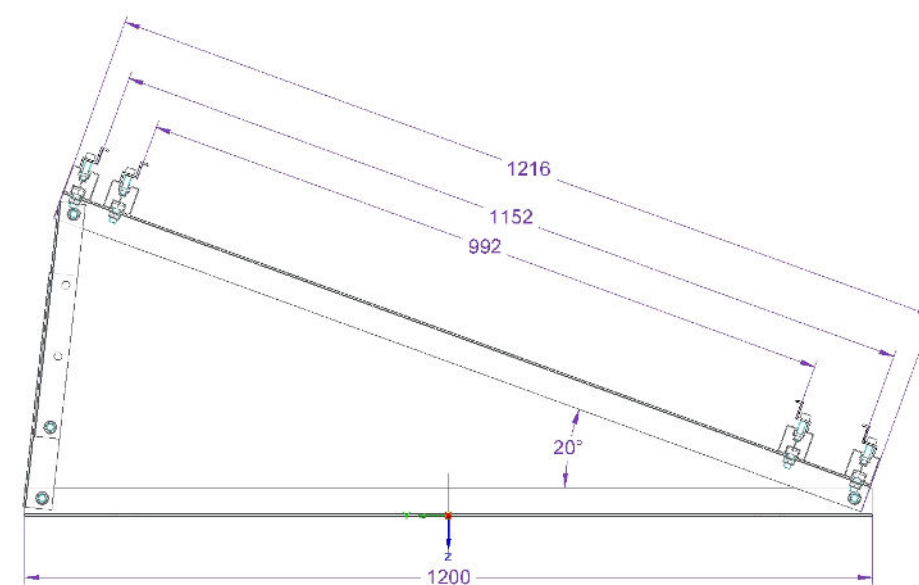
Schemat rozmieszczenia konstrukcji wsporczej
